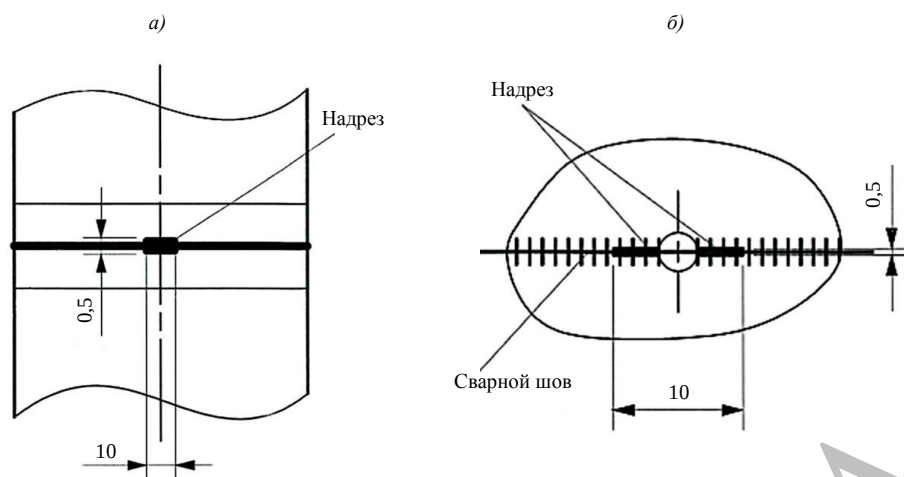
Схема расположения концентраторов напряжений на конструктивно-подобном образце: а – надрез; б – надрез с отверстием диаметром 3 мм
